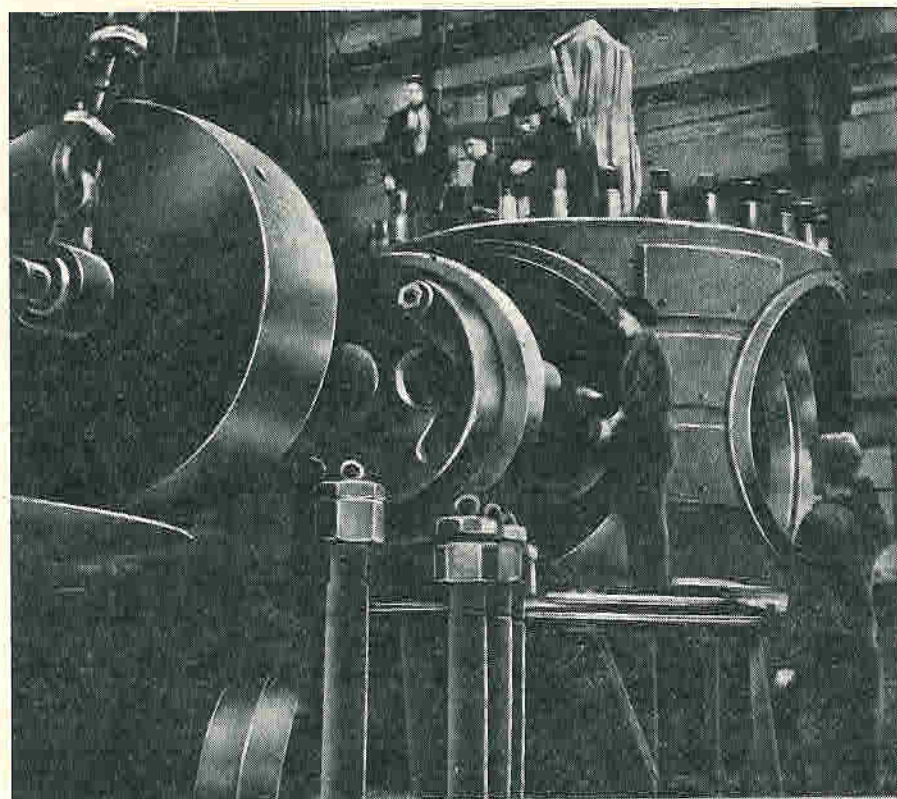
Установка цапф рабочего колеса с помощью специального приспособления с противовесом
